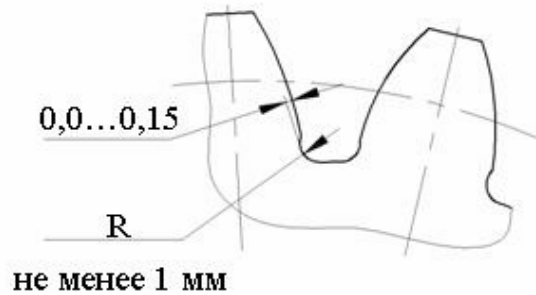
Цилиндрическое эвольвентное зубчатое колесо
